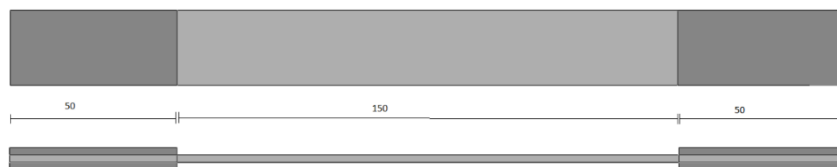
Dimensions (en mm) et géométrie des éprouvettes.
